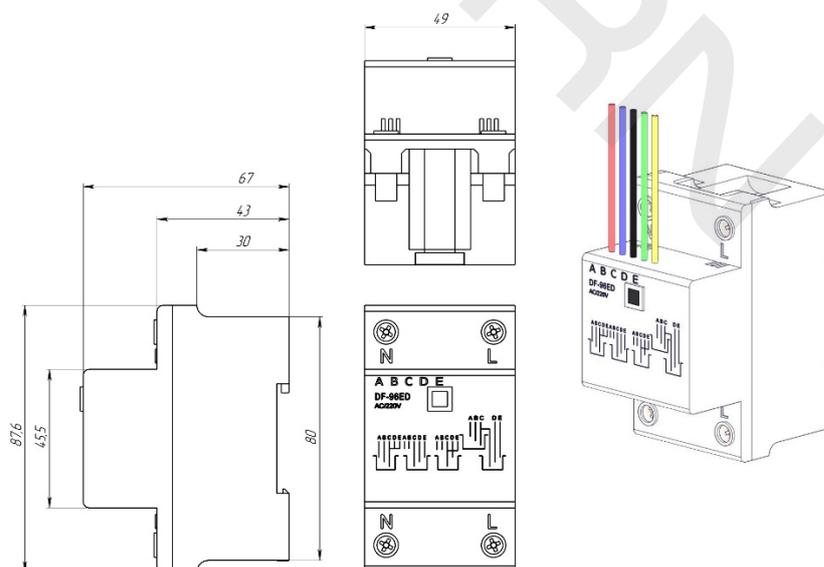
Габаритные размеры контроллера НК-У.
